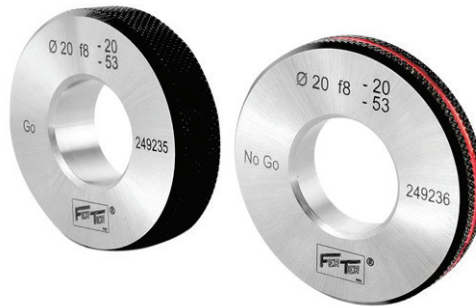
Калибры-кольца для контроля гладких цилиндрических поверхностей [4]
